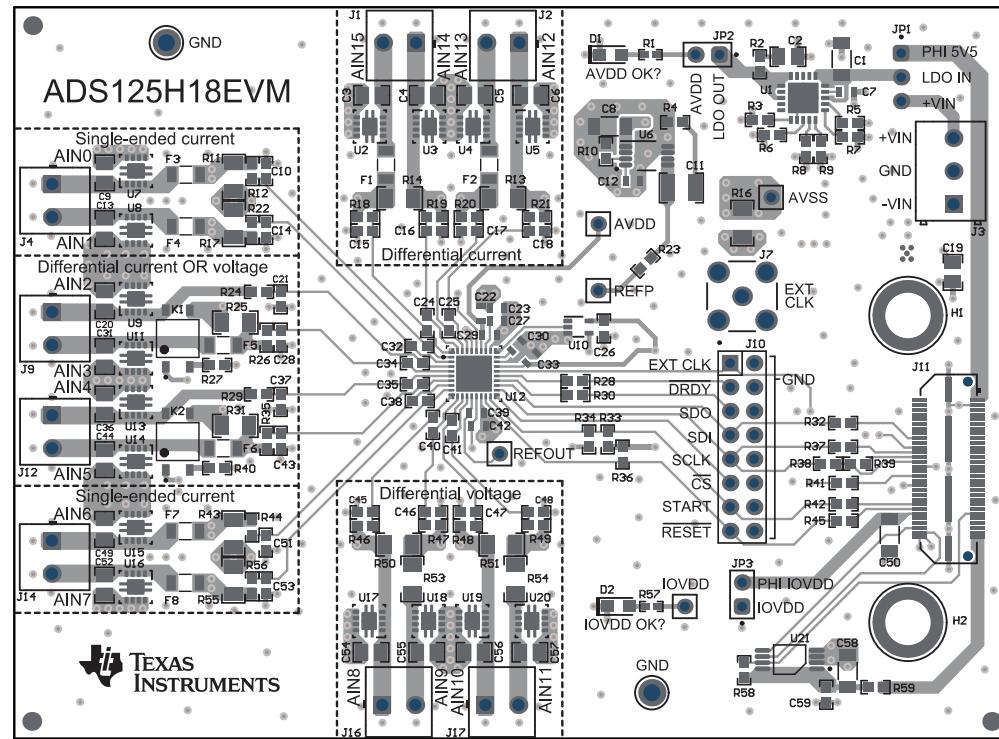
ADS125H18 評価基板 PCB レイアウト—上面層
